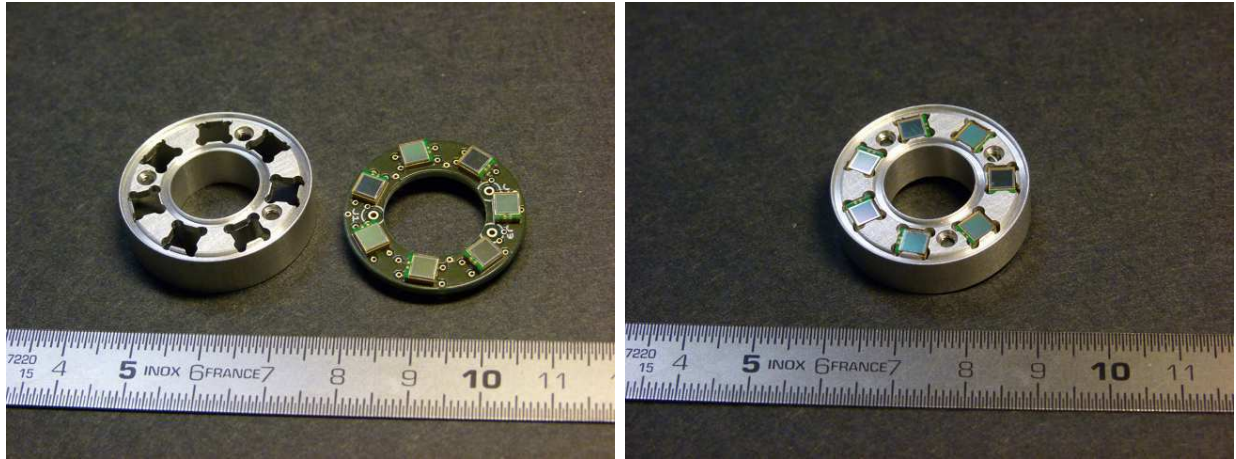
Pièce mécanique de couplage et PCB des SiPM avant (gauche) et après montage (droite)
